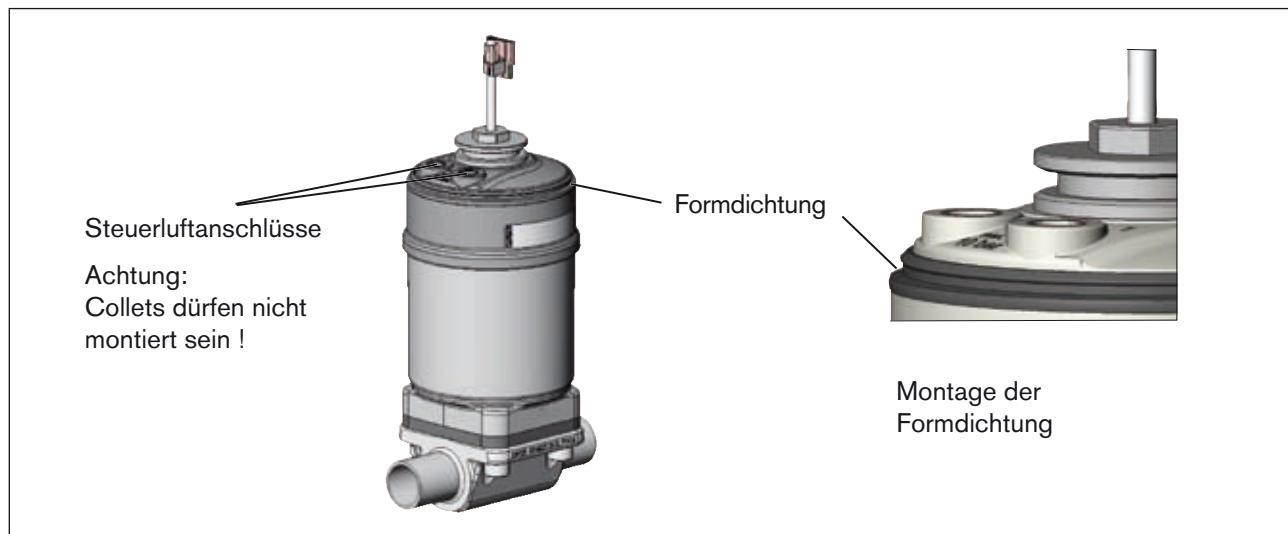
Montage der Dichtringe, Reihe 2103, 2300 und 2301
